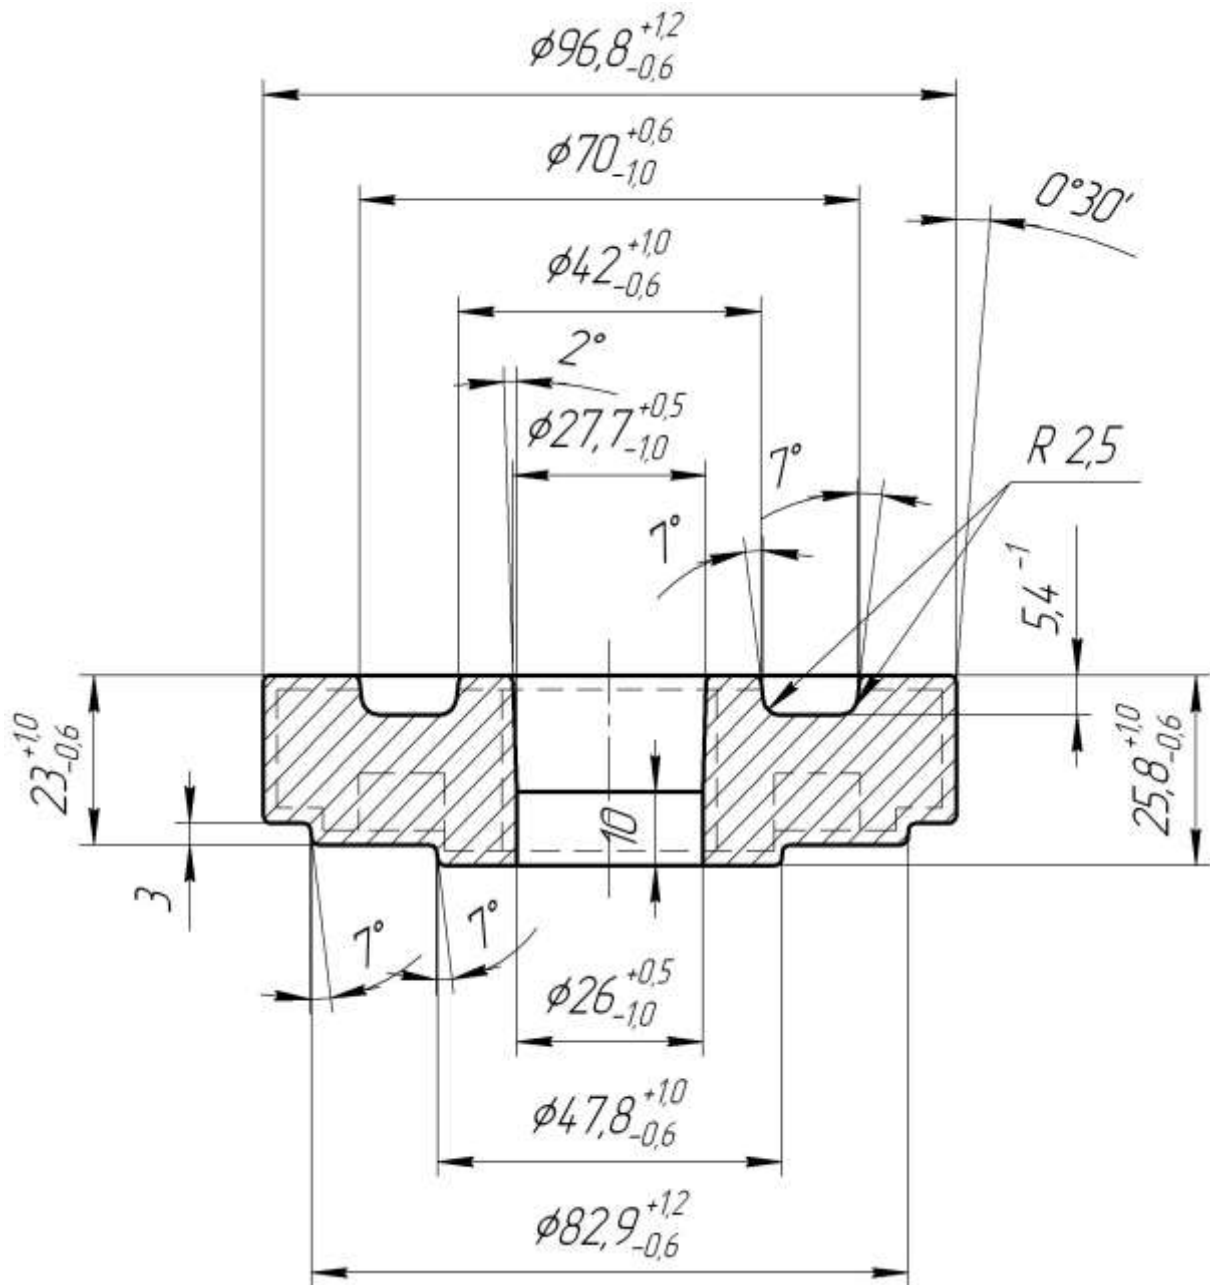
Шестерня ведущая 5-й передачи (заготовка)
